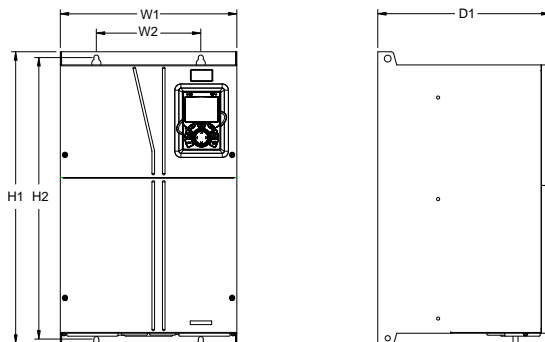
Схема настенного монтажа ПЧ 660 В, от 22 до 132 кВт
